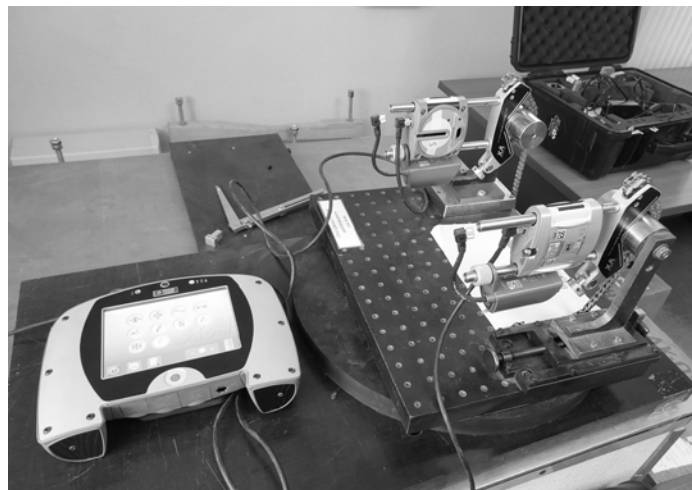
Внешний вид системы Fixturlaser, установленной на стенде для поверки центровщиков
